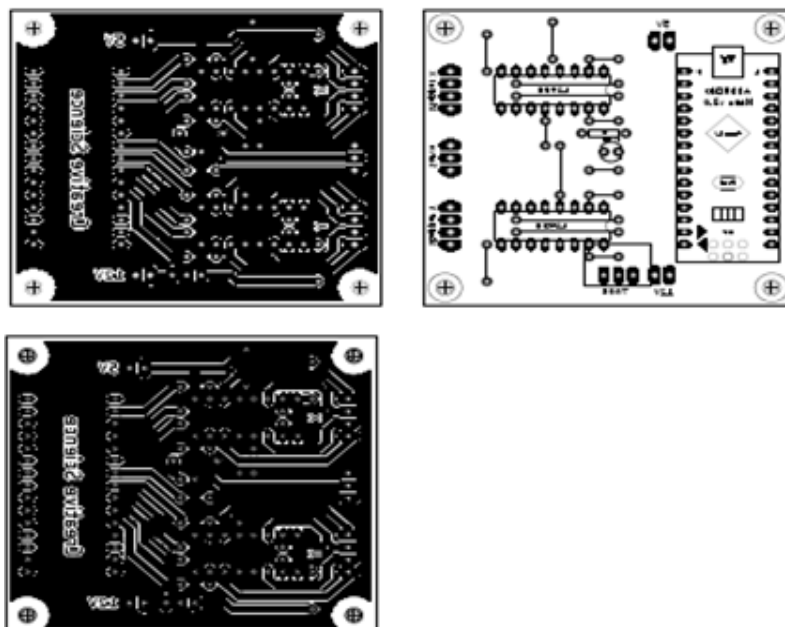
Верхний, нижний слои платы и сборочный чертеж
